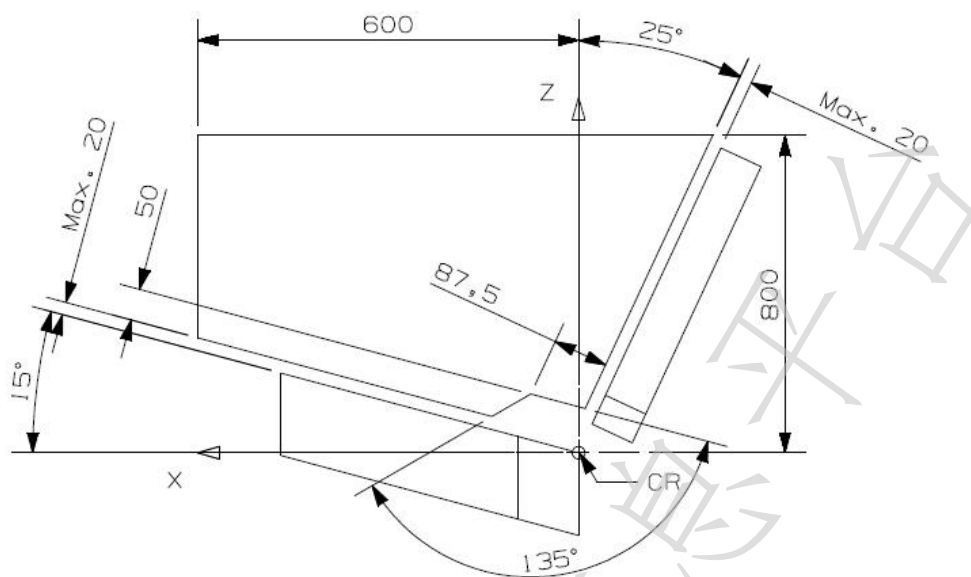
门板几何尺寸——侧视图（公差：±2mm、±1°）
